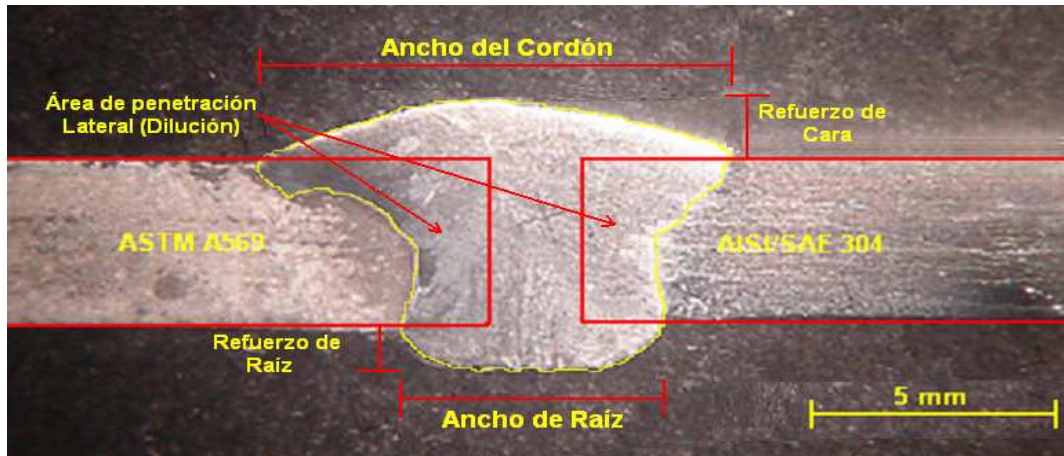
Parámetros geométricos del cordón de soldadura.
